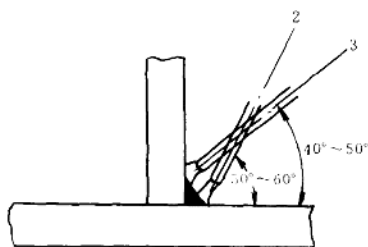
T 形接头平角焊位置焊条电弧焊盖面层时焊条夹角
